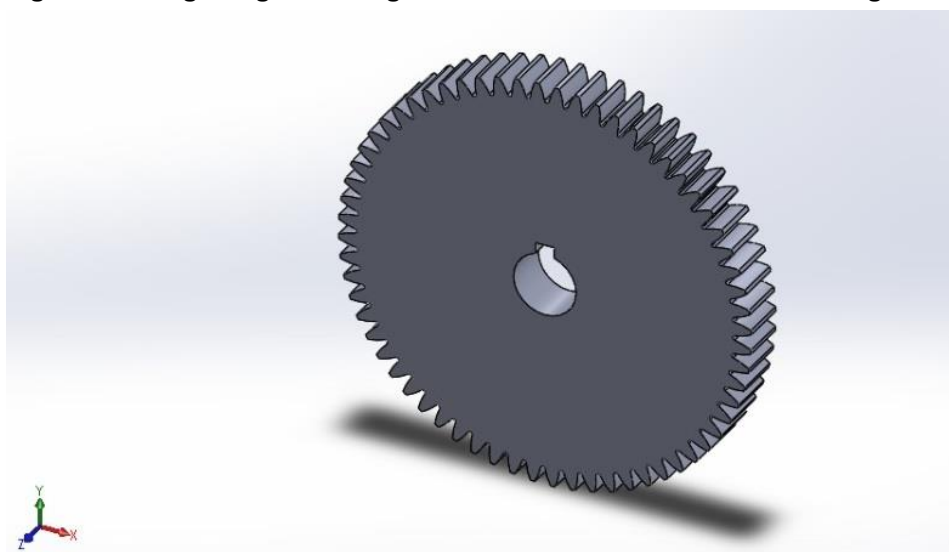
Engrenagem da primeira árvore de transmissão com rasgo de chaveta.
